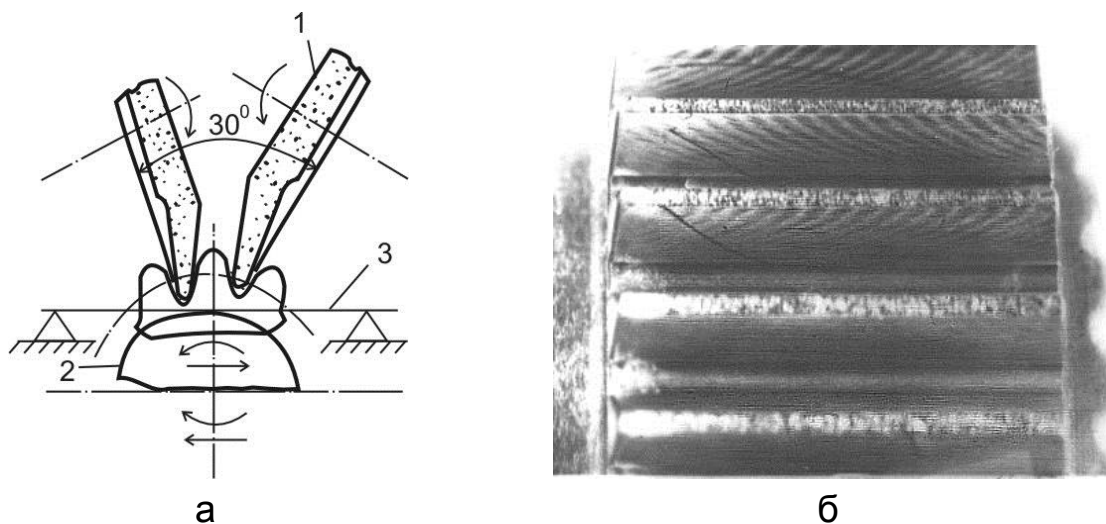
Схема шлифования зубчатого колеса на станке МААГ (5851) с 15-градусной настройкой кругов (а); внешний вид прижогов (б): 1 – тарельчатый шлифовальный круг; 2 – обкатной барабан; 3 – ленты
